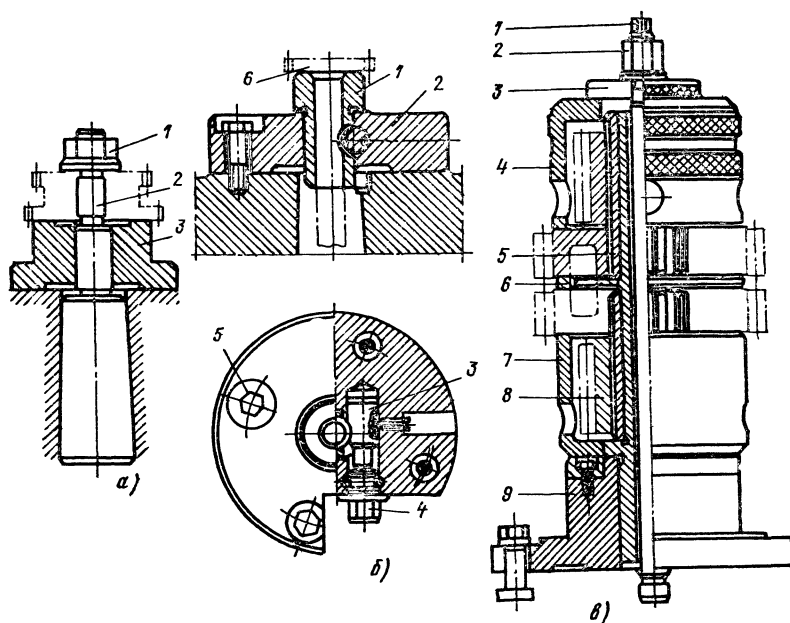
Переналаживаемые приспособления для обработки зубьев колес на зубодолбежных станках
